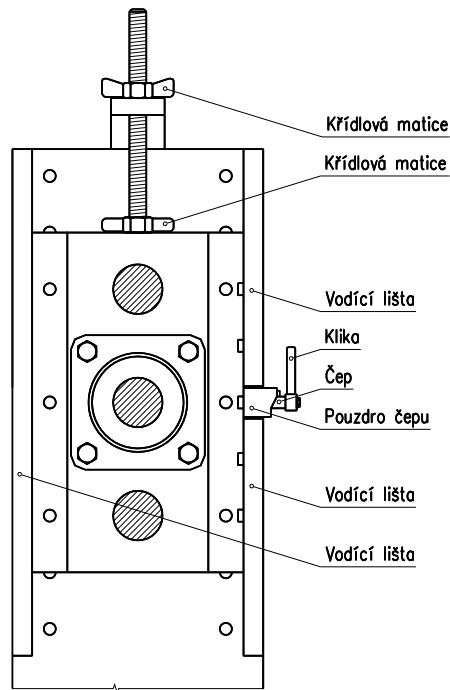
Zajištění přesného posuvu kulisy pomocí zajišťovacího čepu
